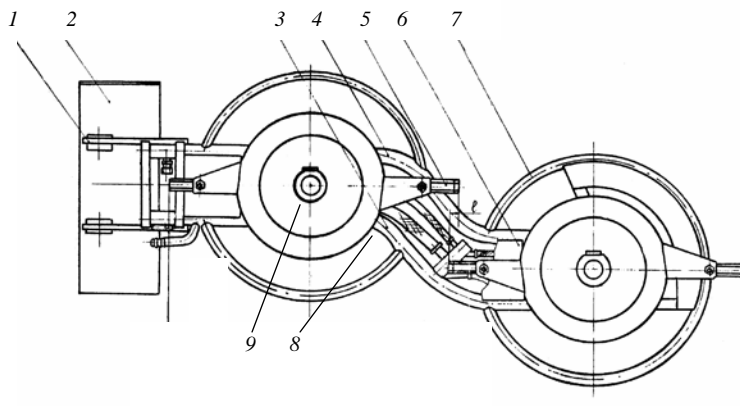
Двухроторный рабочий орган: 1 – проушины; 2 – узел присоединения;
